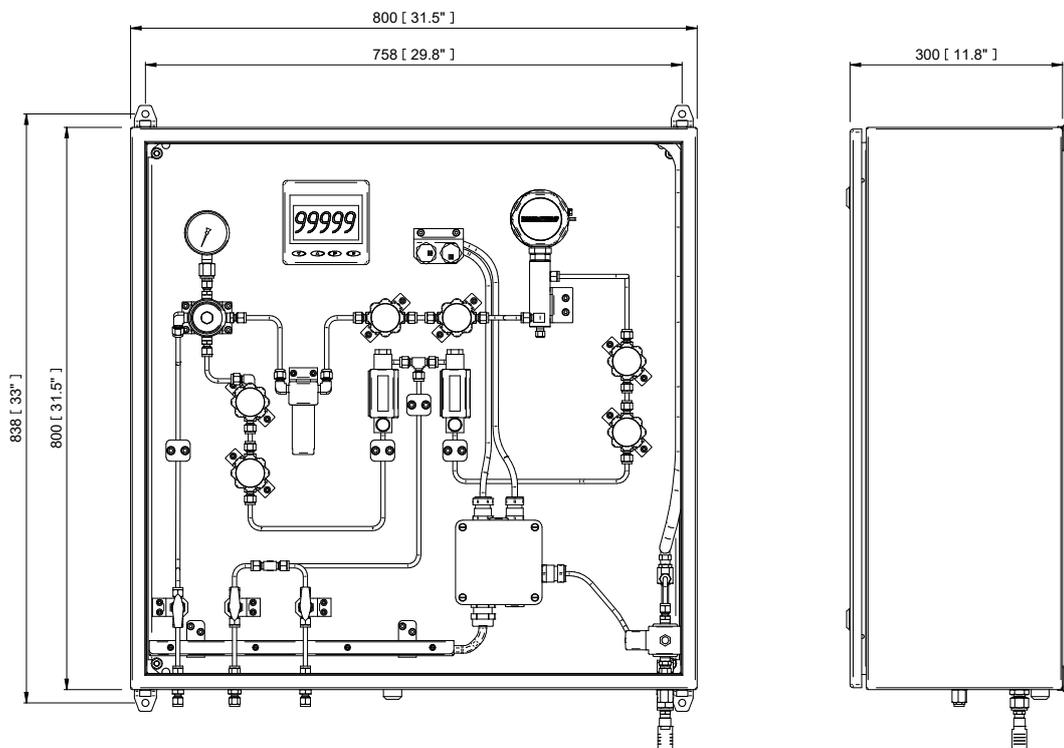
Abmessungen des Gehäuses für Außenmontage
